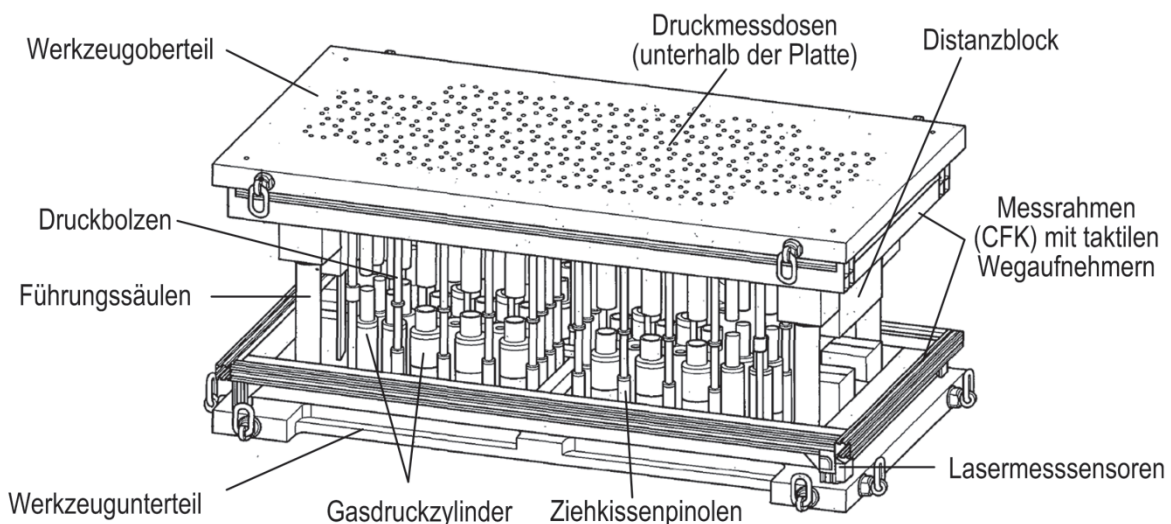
Prüfwerkzeug zur Ermittlung der Eigenschaften einer Umformpresse [110]
